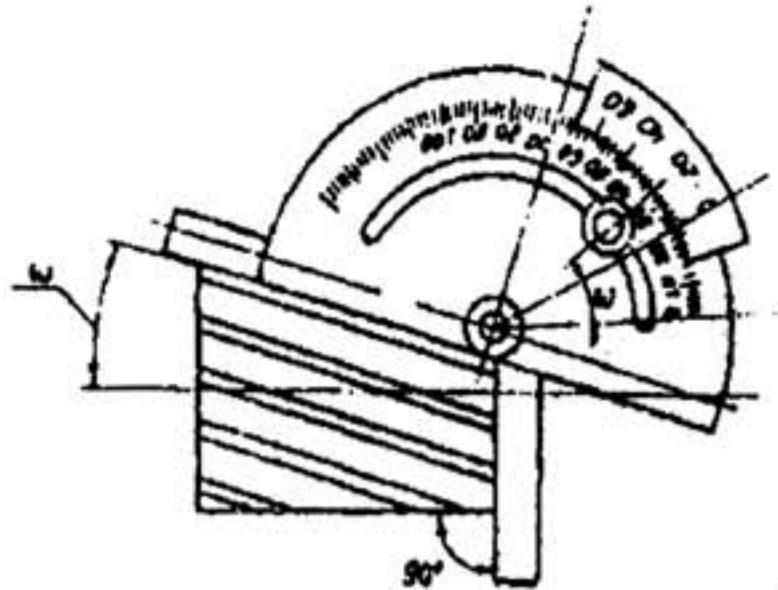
Измерение угла наклона винтовой канавки ω цилиндрической фрезы
